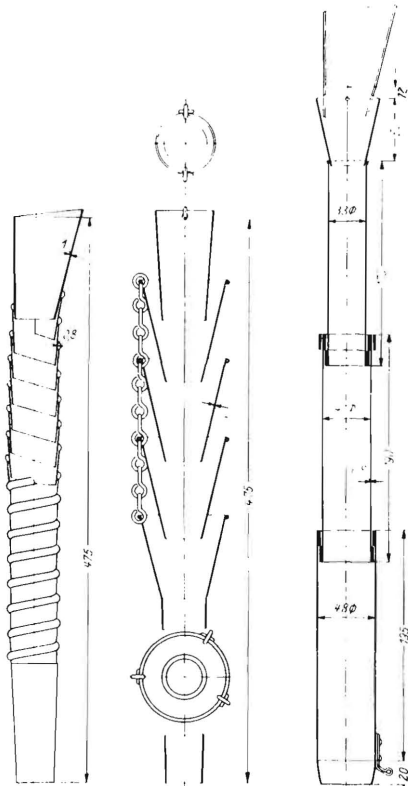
Die seitherigen Saatlösungsrohre für Drillmaschinen aus Stahl können mit Vorteil durch PVC-Kunststoffschläuche ersetzt werden.
